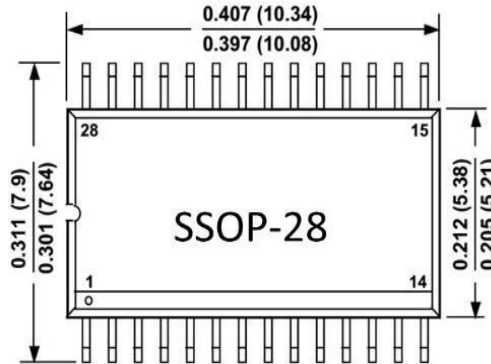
Dimensiones y encapsulado del CI AD9850 en milímetros
